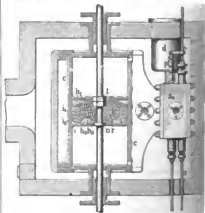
Kornbörfers Dichtung und Schmierung einer Heißluftmaschine.
